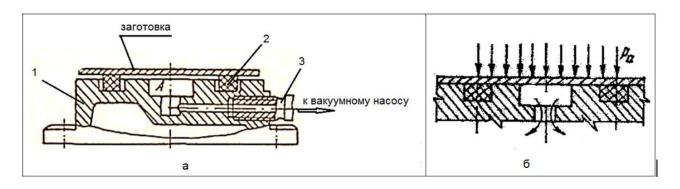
Станочное приспособление с применением вакуума: а – установка заготовки; б – закрепление заготовки
